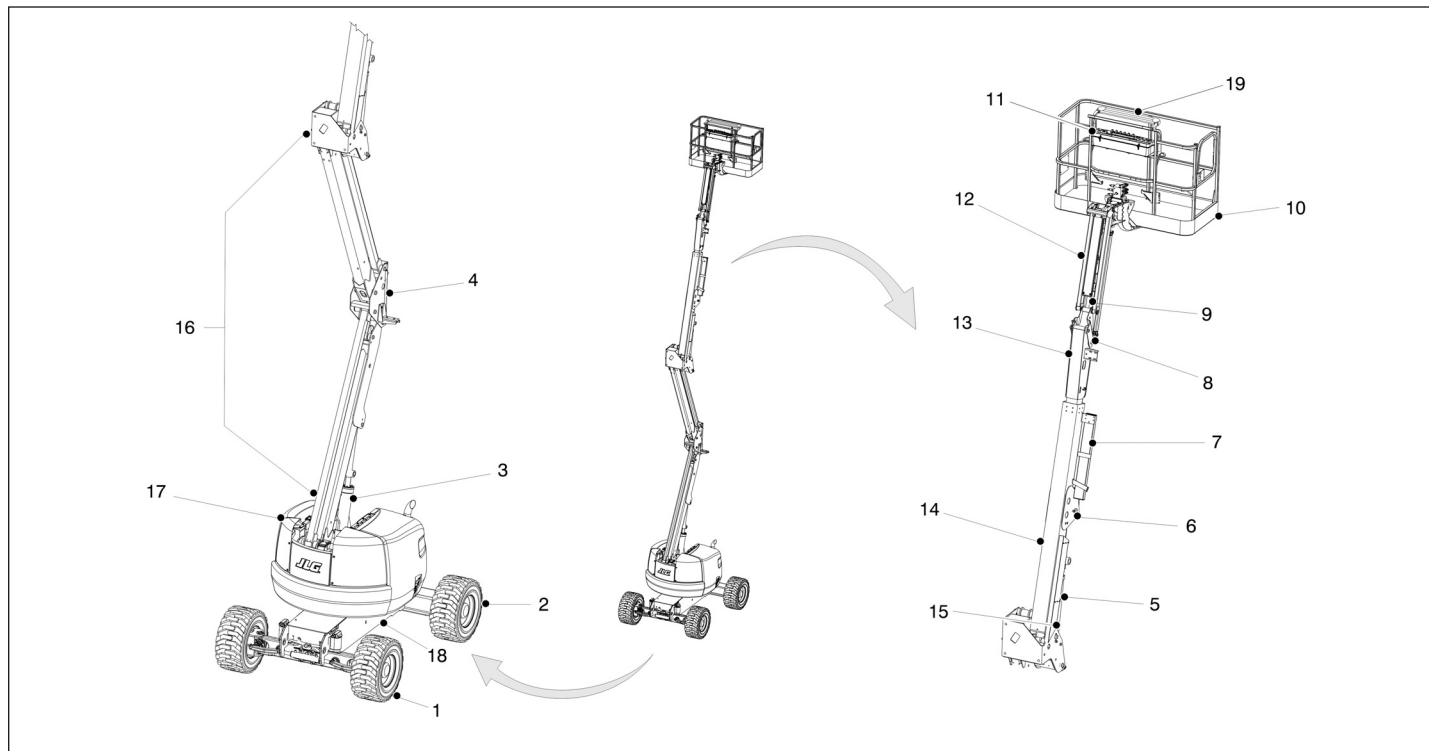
Grundläggande nomenklatur – blad 1 av 2
